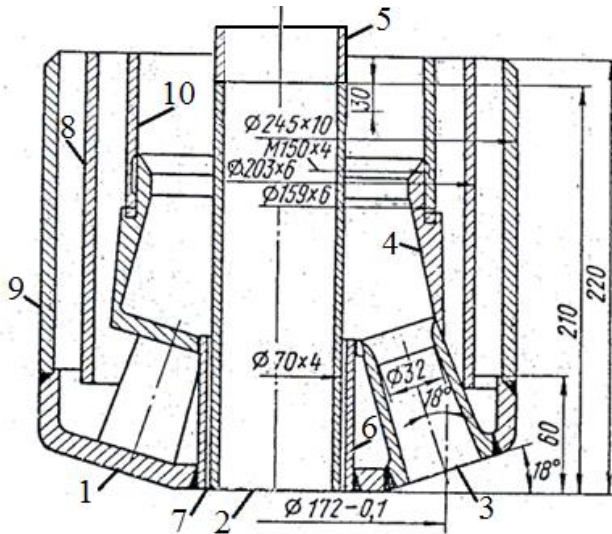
Конструкція зварної головки паливно-кисневої фурми-пальника [3,4] для нагріву брухту і продувки ванни в 160-т конвертері: 1- головка; 2- центральне газове сопло; 3- кисневі сопла; 4- киснева камера; 5- центральна труба підведення природного газу; 6- металевий стакан; 7- кільцевий зазор для проходження кисню; 8, 9- патрубки підведення і відведення охолоджуючої води відповідно; 10- труба підведення кисню
